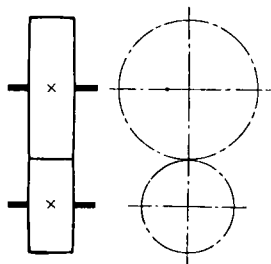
Условное обозначение зубчатой цилиндрической передачи с наружным зацеплением (показываются только делительные окружности)
